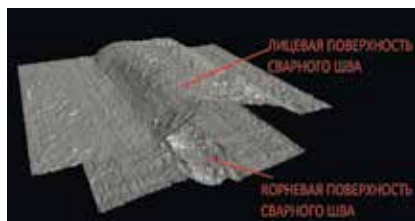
Цифровые реплики лицевой и корневой поверхностей сварного шва
